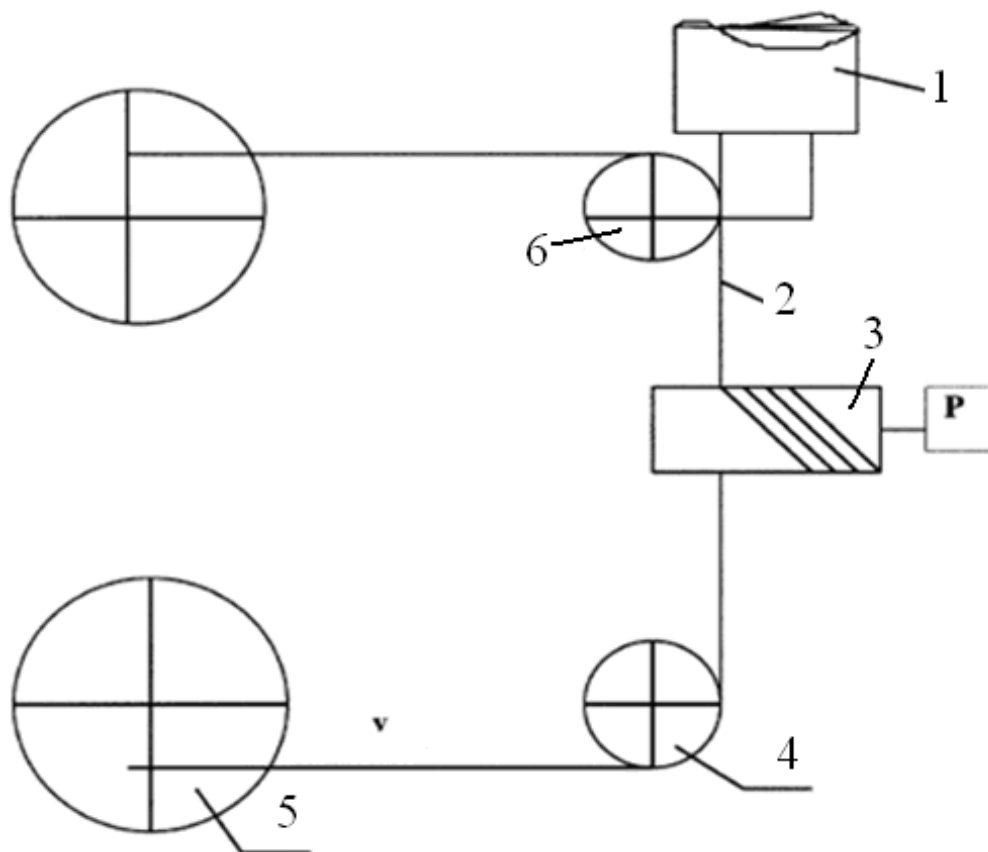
Схема ультразвуковой обработки непрофилированным инструментом – проволокой: 1 – концентратор; 2 – инструмент – проволока; 3 – обрабатываемая деталь; 4 – направляющий ролик; 5 – катушка; 6 – прижимной ролик
